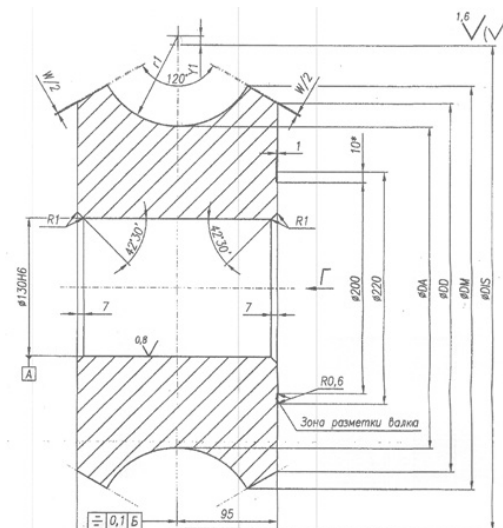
Общий вид отливки «Трубопрокатный валок» из чугуна ТШХН-50 [1]
